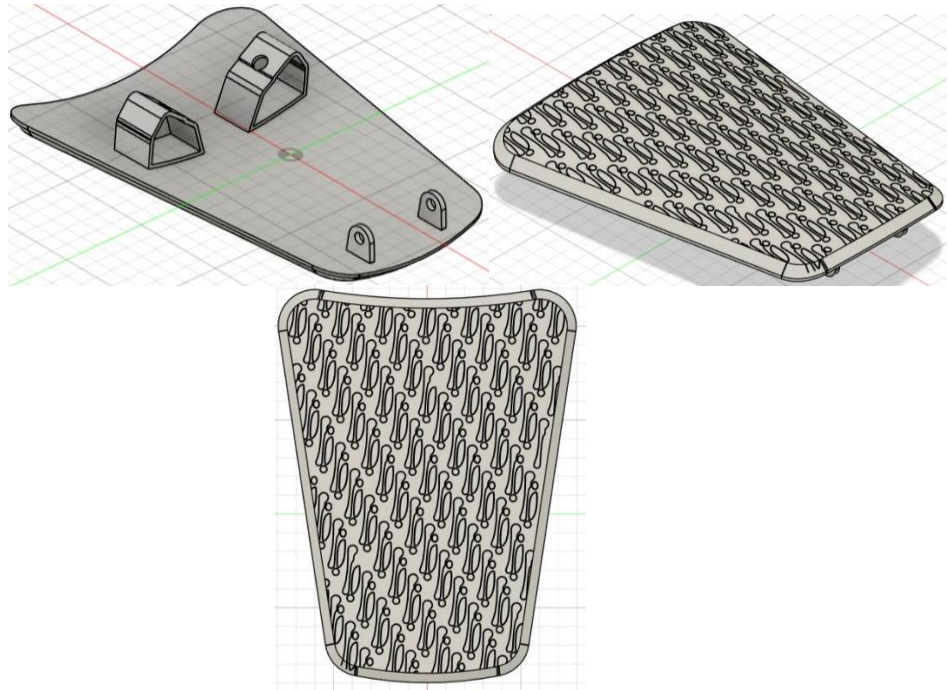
14 Hasil *Redrawing* dan hasil 3D scan disejajarkan
